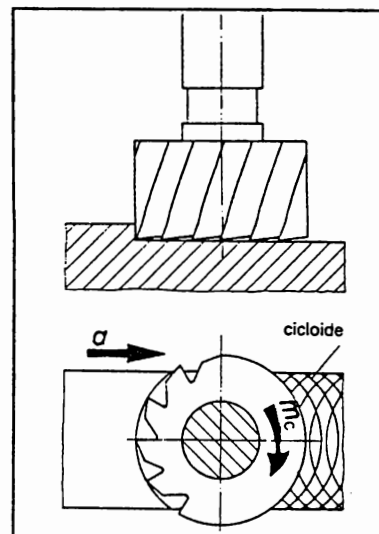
Fresado de una superficie plana elaborada por una fresa frontal con el eje perpendicular.
